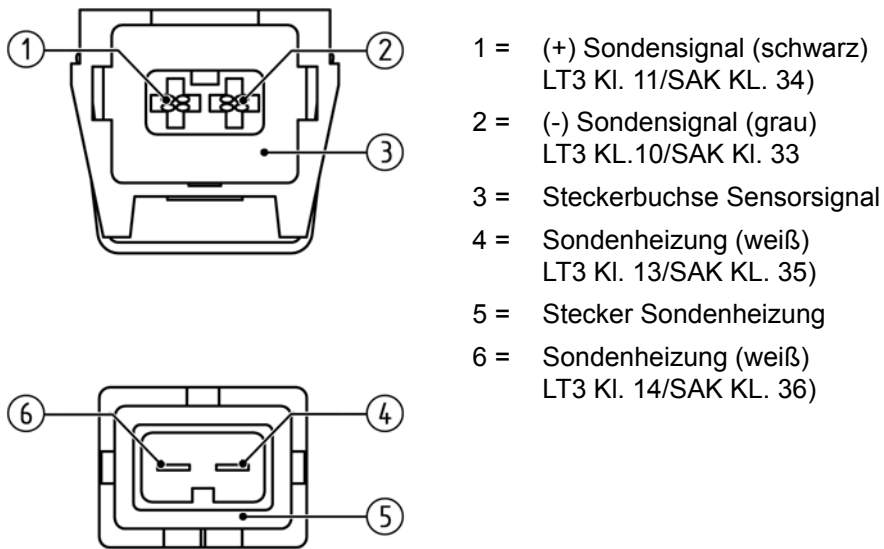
Anschlussbelegung Sondenanschlusstecker
